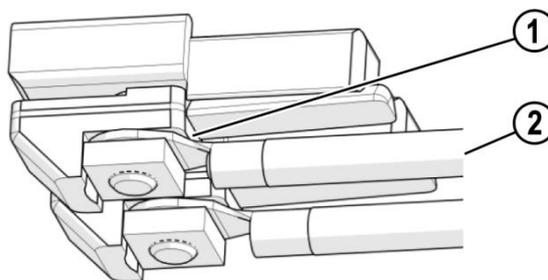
Einspeiseklemmen mit Quetschkabelschuh (1),
